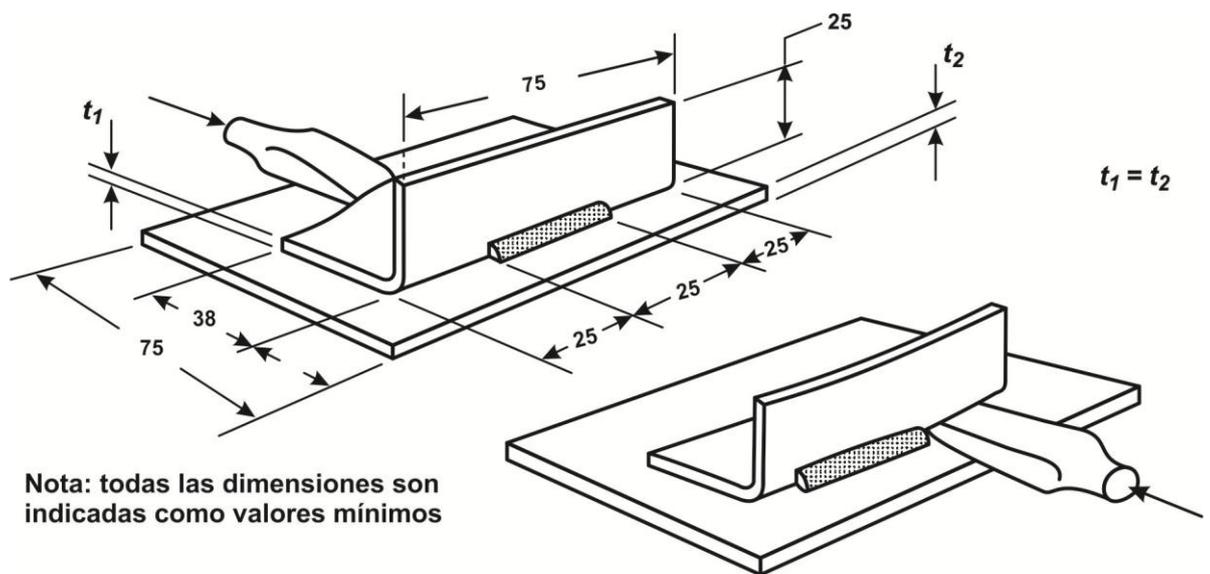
a). Esquema de ensayo para soldaduras entre chapas con junta acampanada simple.
